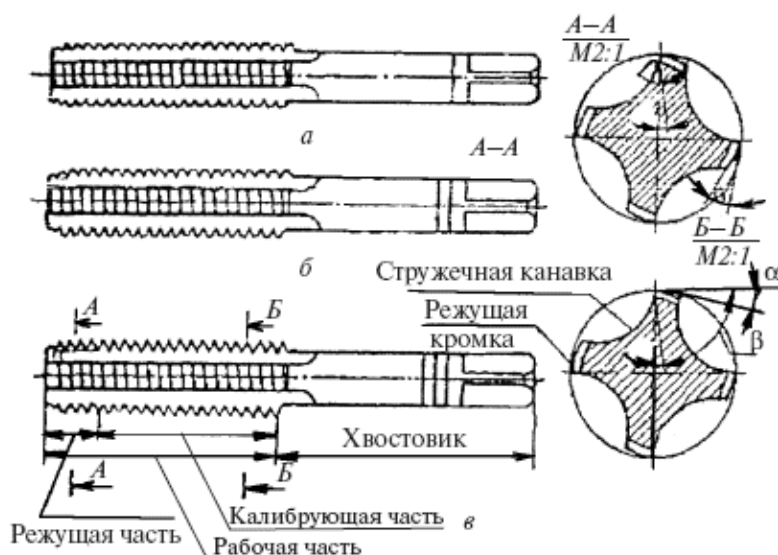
Метчики ручные слесарные: а – черновой; б – средний; в – чистовой
